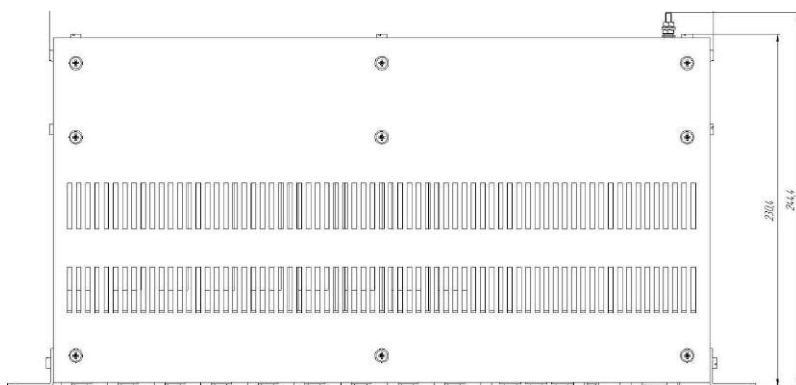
Габаритные размеры контроллера СГМ ЭРИС-110 (крейтовая модель)
